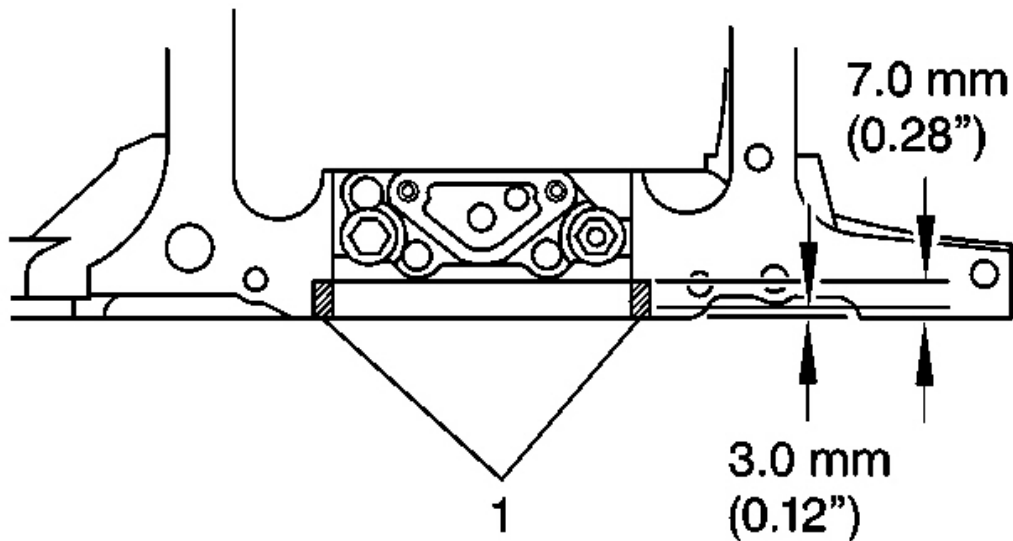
Vista del cárter de aceite y tornillos de cortesía de General Motors Corp.
